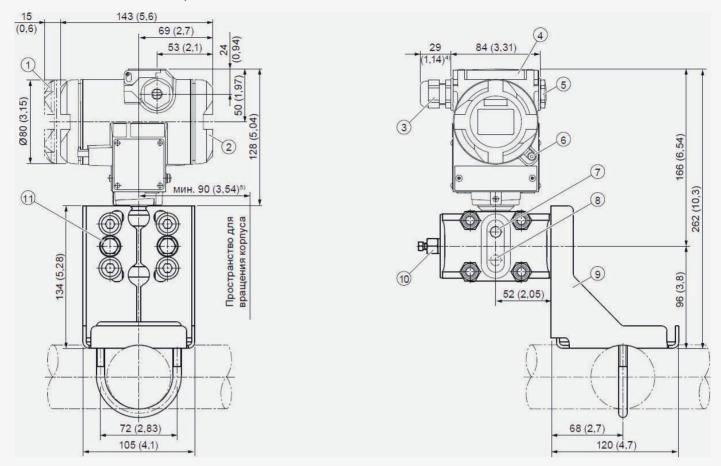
Измерительный преобразователь КМ35 в корпусе дифференциального давления, размеры в мм (дюймах)
